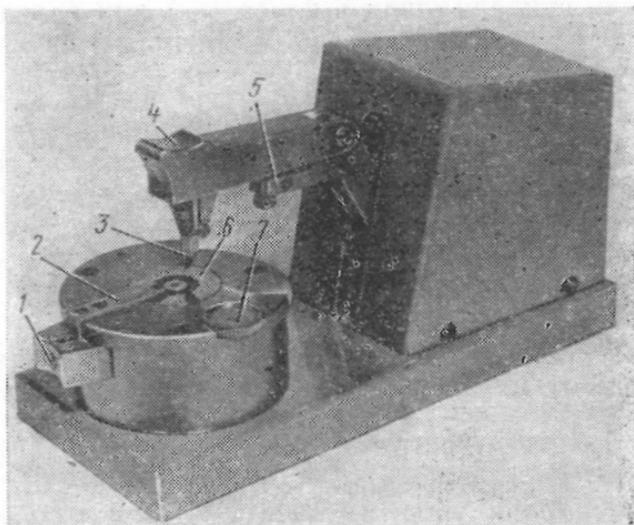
Приспособление для отрезки внешнего витка спирали:
